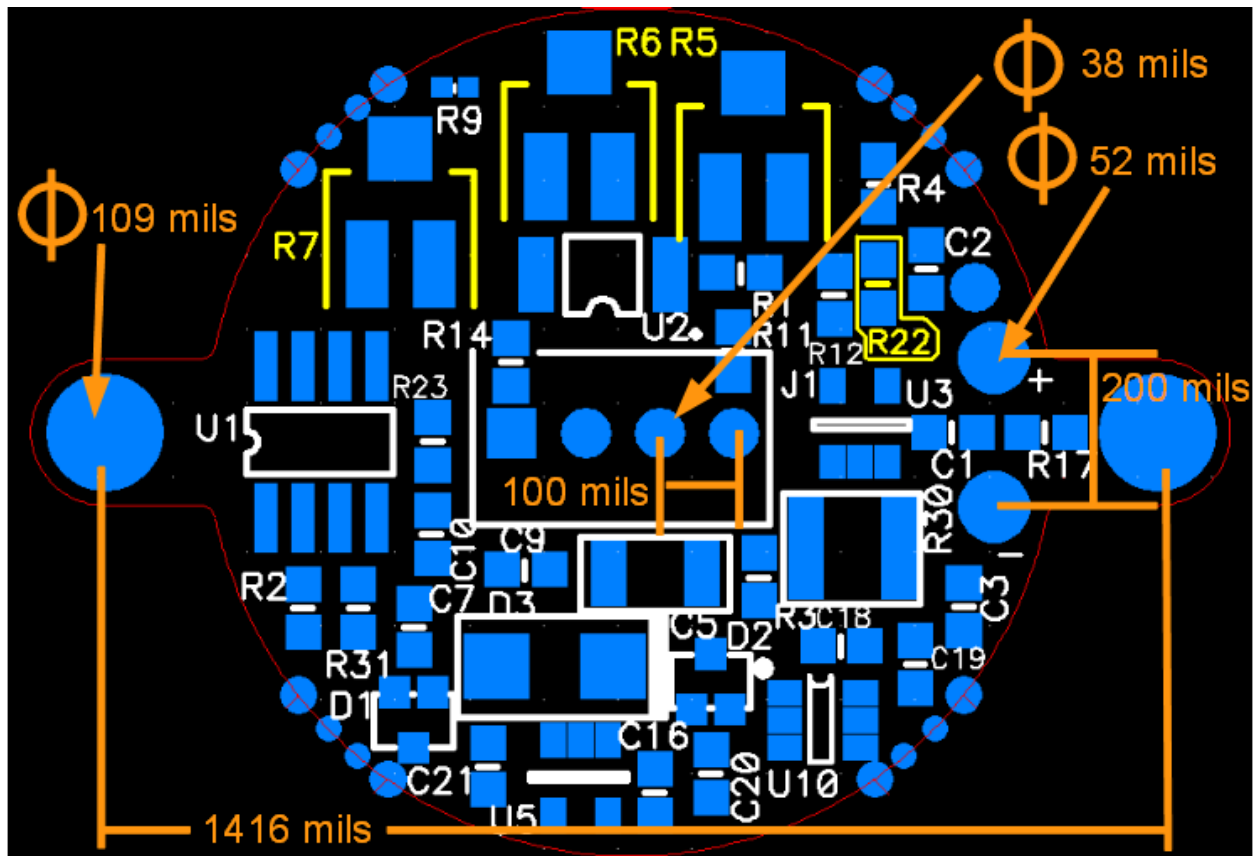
Vue du côté potentiomètre du PCB OEM.
